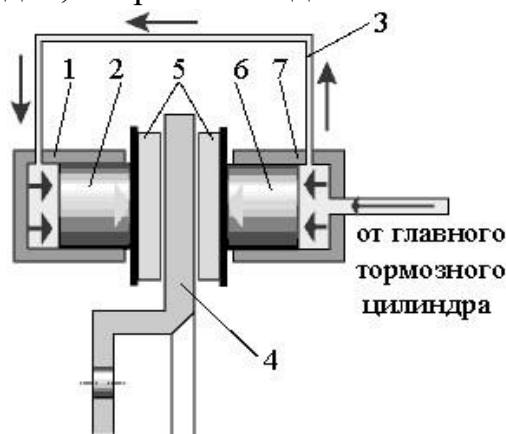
Схема работы дискового тормозного механизма с неподвижным суппортом: 1 - наружный рабочий цилиндр (левого) тормоза; 2 - поршень; 3 - соединительная трубка; 4 - тормозной диск переднего (левого) колеса; 5 - тормозные колодки с фрикционными накладками; 6 - поршень; 7 - внутренний рабочий цилиндр переднего (левого) тормоза.
